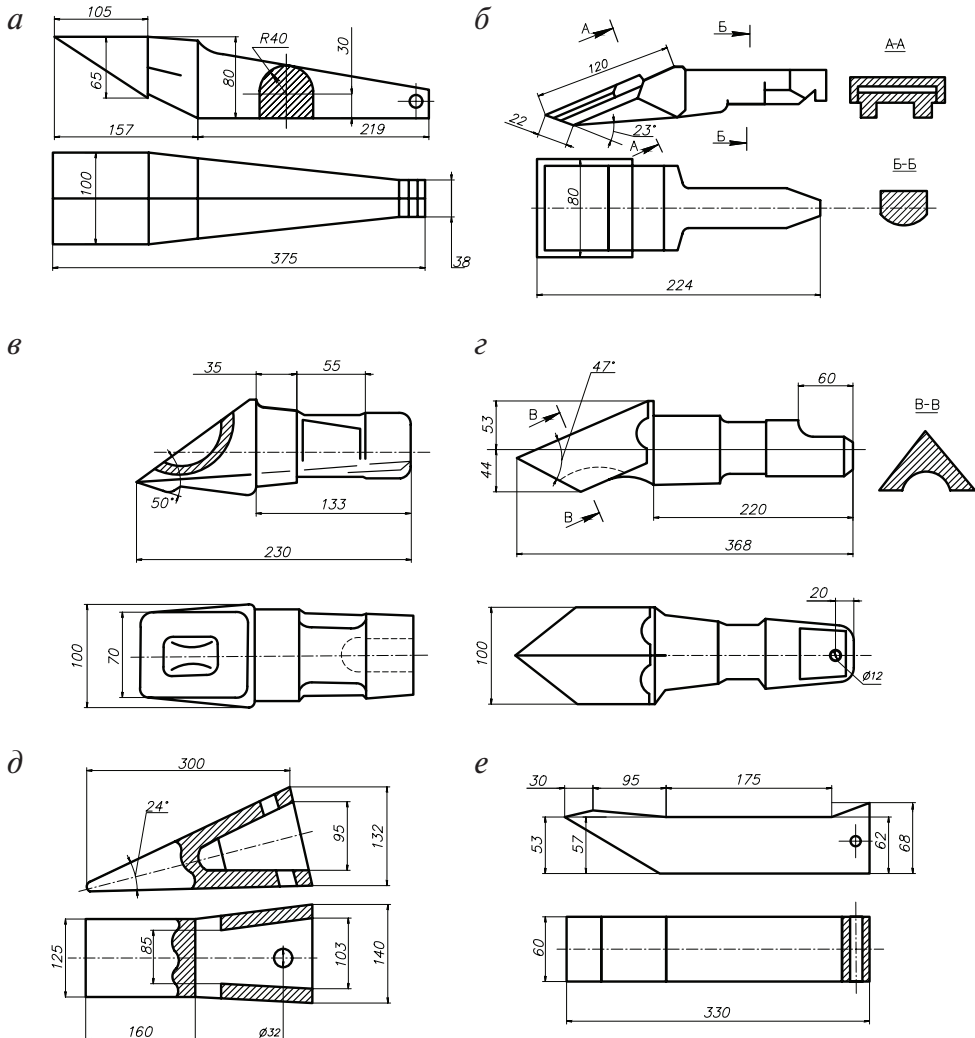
Резцы и коронки роторных экскаваторов:
